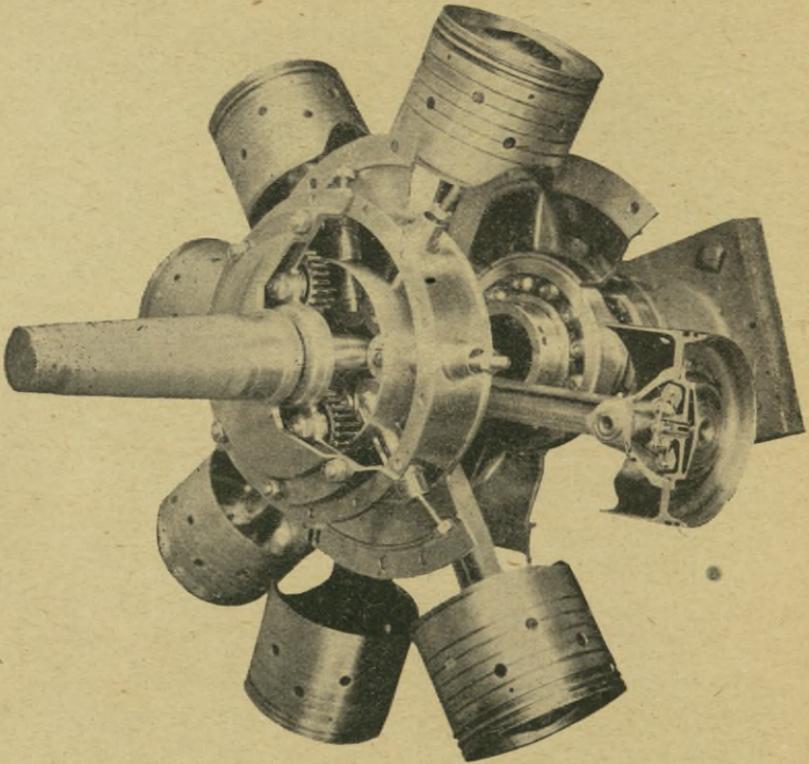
Kurbelwelle mit Kolben und Gehäuse eines 80 PS Gnom-Motors.
